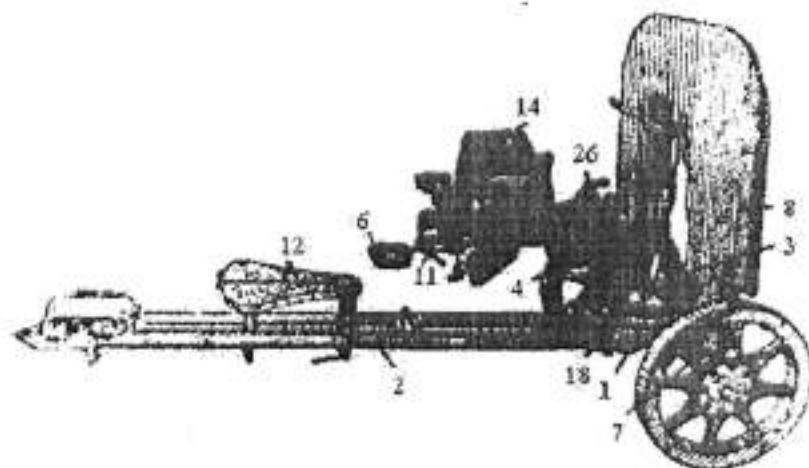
Общий вид станка (в положении для наземной стрельбы)
